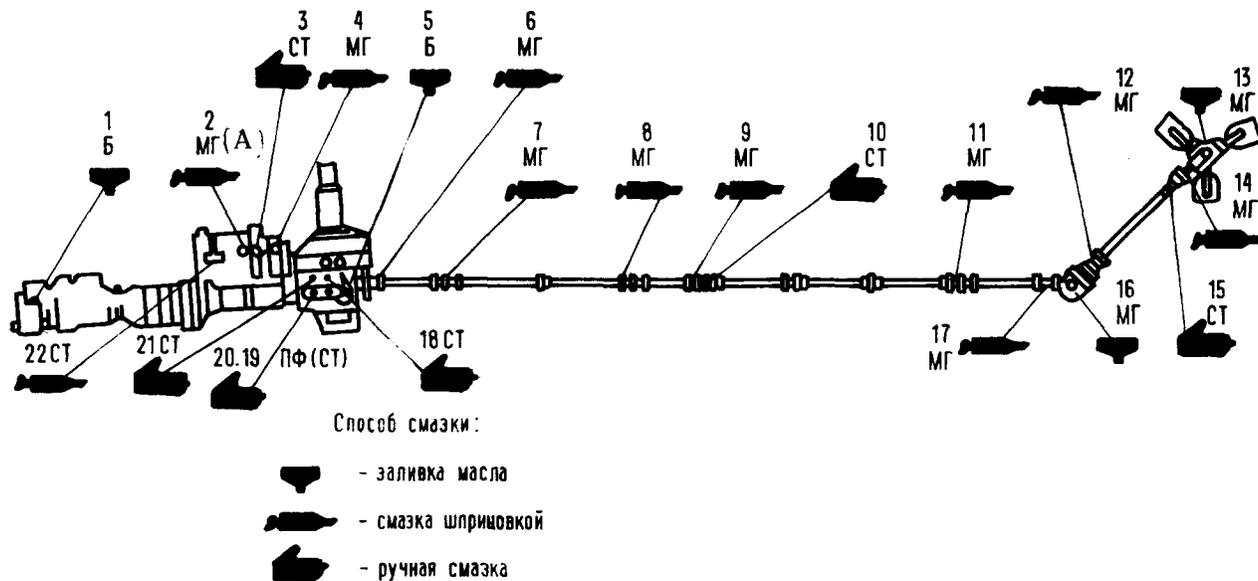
Точки смазки двигателя и агрегатов трансмиссии:
